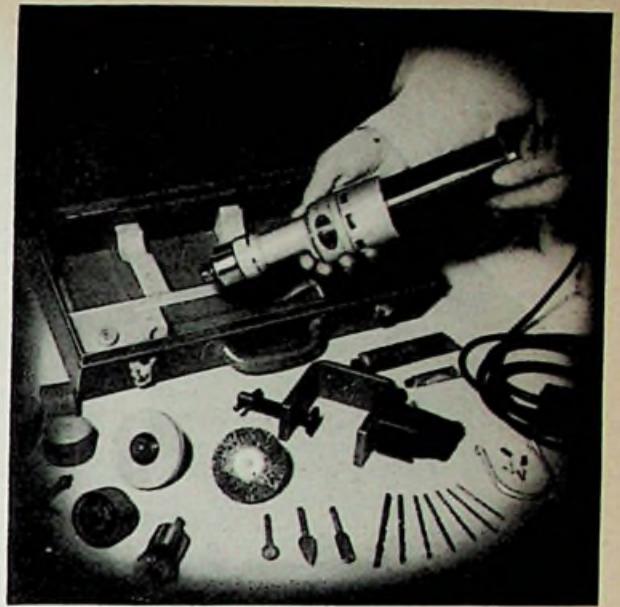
Bosch-Combi-Elektrowerkzeug mit Zubehör
